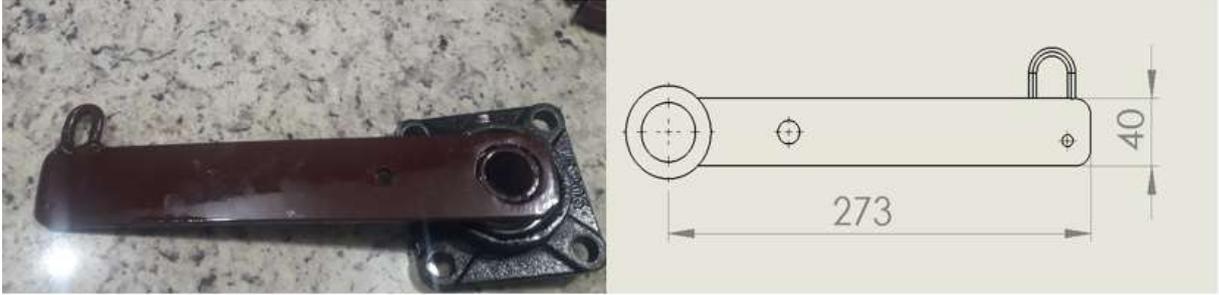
Conjunto montado com eixo, mancais e rolamentos
